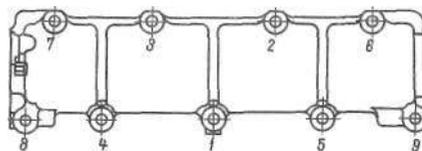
Порядок затяжки гаек корпуса подшипников распределительного вала
